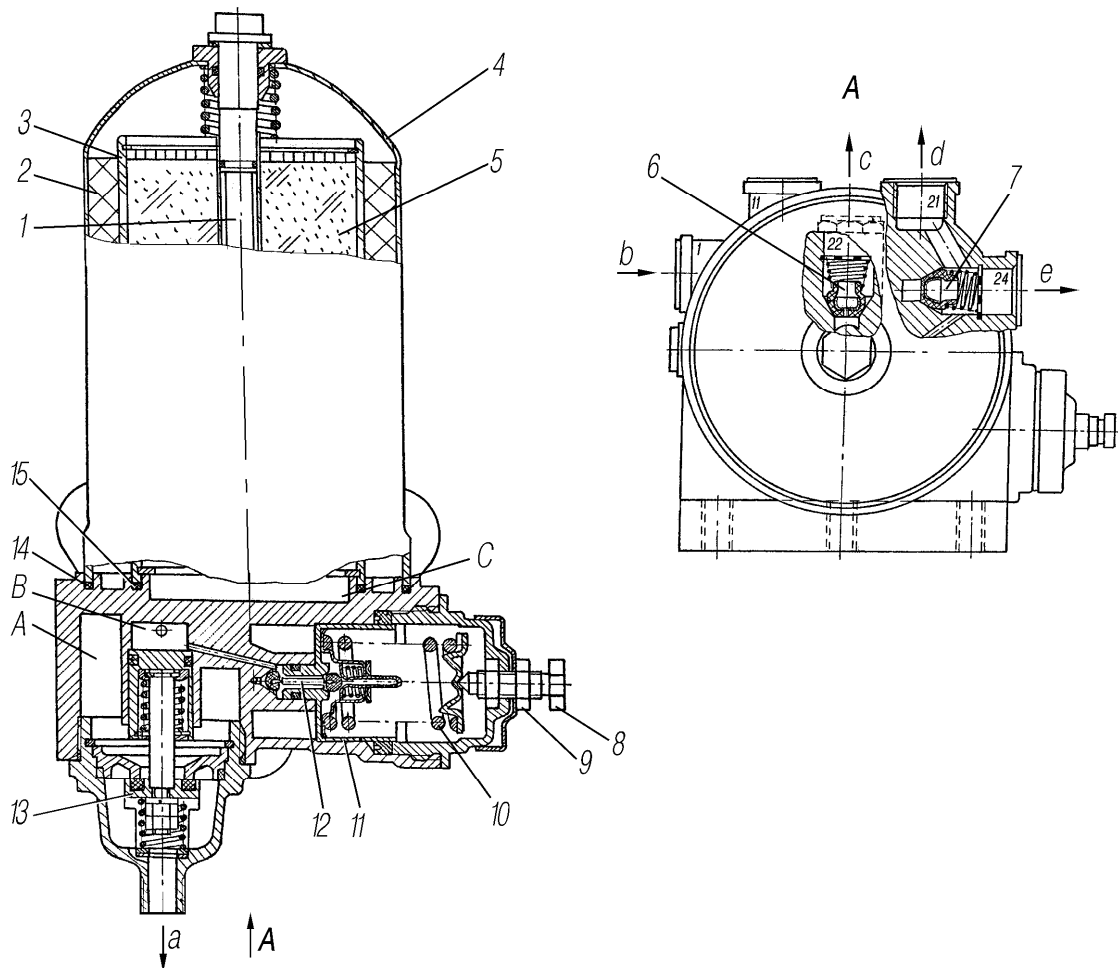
Влагмаслоотделитель со встроенным регулятором давления: 1- винт; 2- фильтр; 3- стакан; 4- колпак; 5- элемент адсорбирующий; 6- дроссель; 7- клапан обратный; 8- винт регулировочный; 9- контргайка; 10- пружина; 11- уравнивающий поршень; 12- клапан впускной; 13- клапан разгрузочный; 14,15- уплотнительные кольца; А,В,С- полости; а- вывод в атмосферу; б- подвод от компрессора; с- вывод в регенерационный баллон; d,e- вывод в систему
